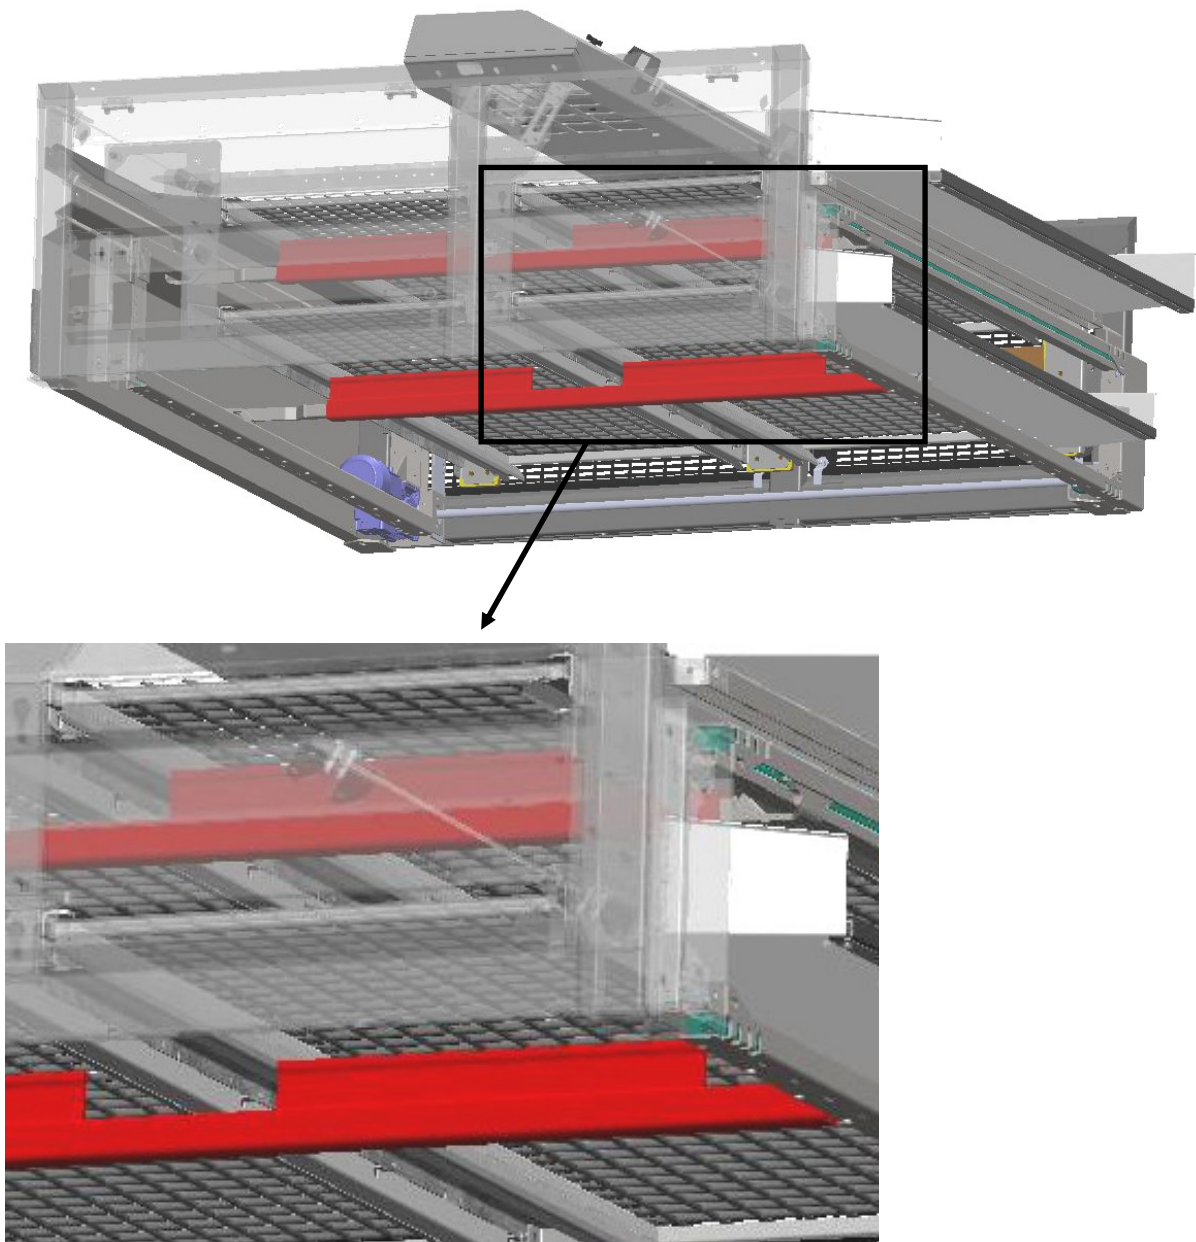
viser placeringen af lænseslangerne der fastholder soldene i soldkassen.
